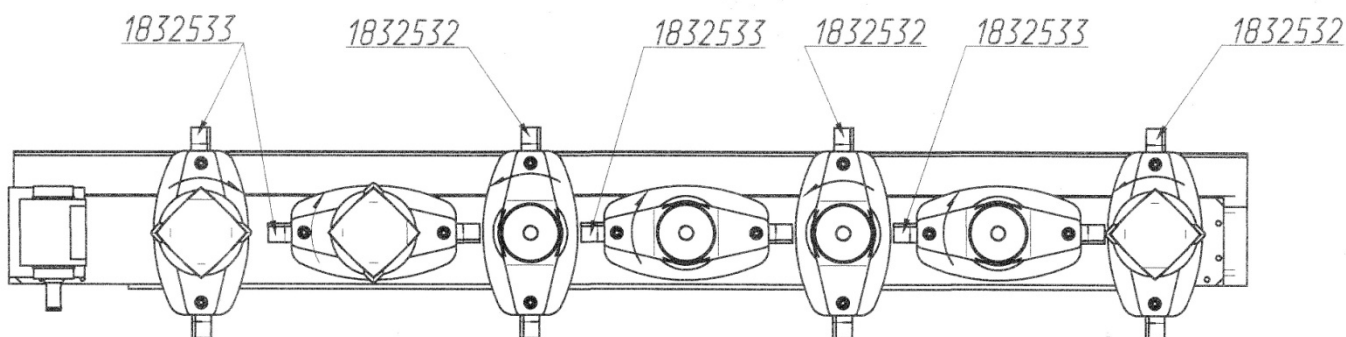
Крепление скашивающего ножа к ротору
